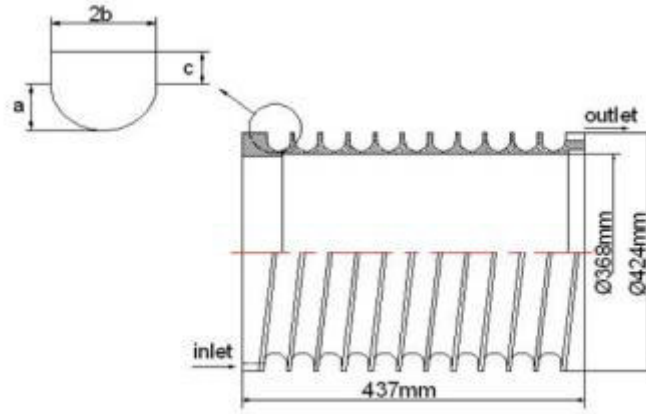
Dimensions de la coque et le chemin d'écoulement du liquide
